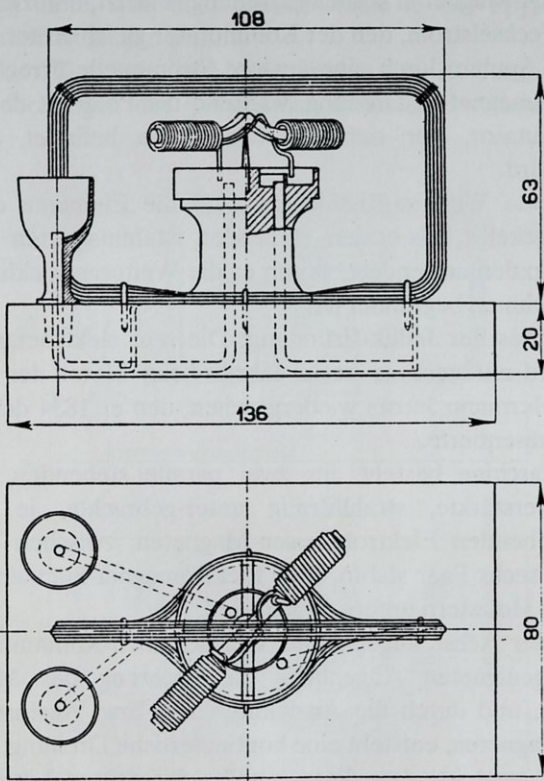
Drehwerk (Urelektromotor), erste Konstruktionslösung, Seitenansicht u. Grundriss
